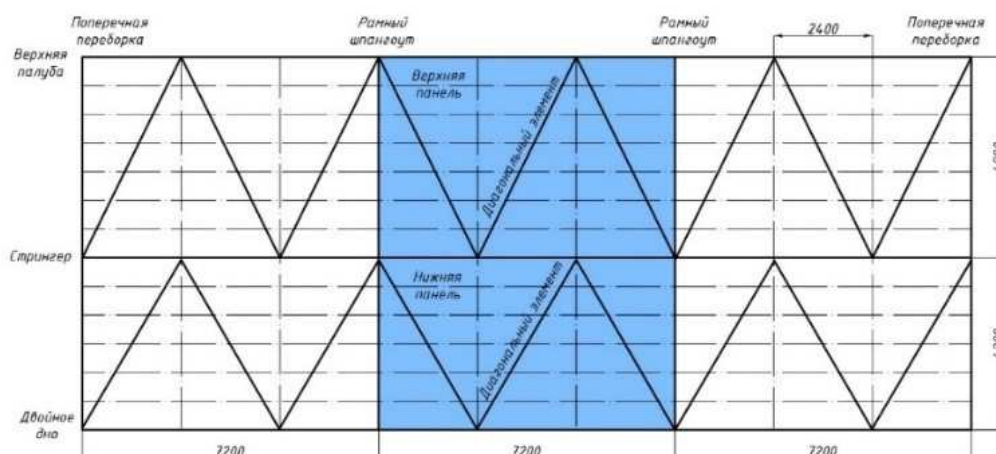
Расчетная схема бортового перекрытия, набранного по продольной системе набора с диагональными элементами
